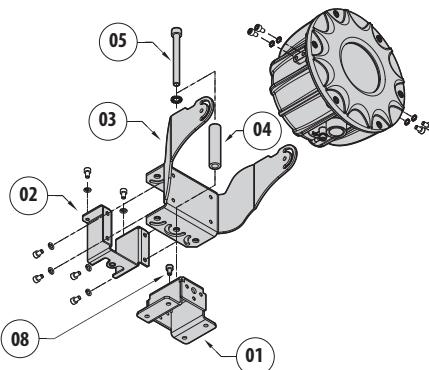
Fissaggio a parapetto con ingresso cavi verso il basso.
